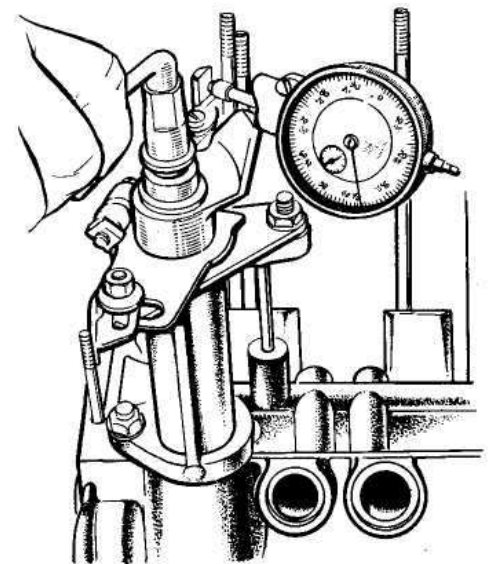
Проверка бокового зазора в зацеплении шестерни привода распределителя при помощи приспособления с индикатором
